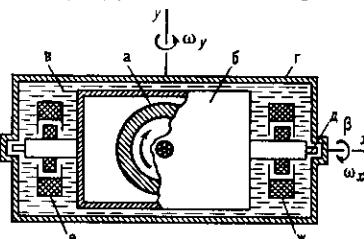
Поплавковый интегрирующий гироскоп: a — ротор гироскопа; b — поплавок, в теле к-рого расположено подшипник оси ротора; c — поддерживающая жидкость; d — корпус; e — стальные панели в камневых опорах; f — датчик угла поворота поплавка относительно корпуса; g — электромагнитное устройство, прилагающее момент вокруг оси поплавка.
